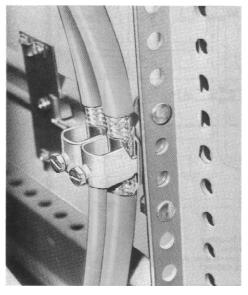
Fissaggio dei cavi schermati con fascette serracavi ed elemento di collegamento per tubi (rappresentazione schematica)
